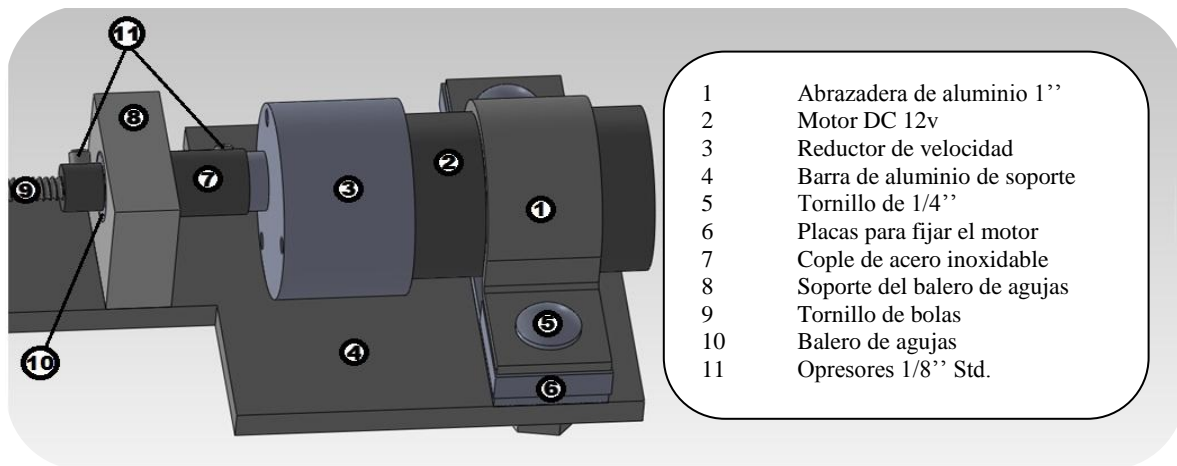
Vista del montaje del motor en *SolidWorks* [25].
